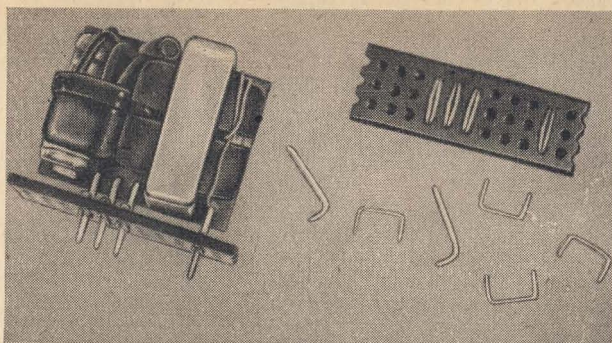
Baugruppe mit Mehrfach-Steckverbindung, einsatzbereit
